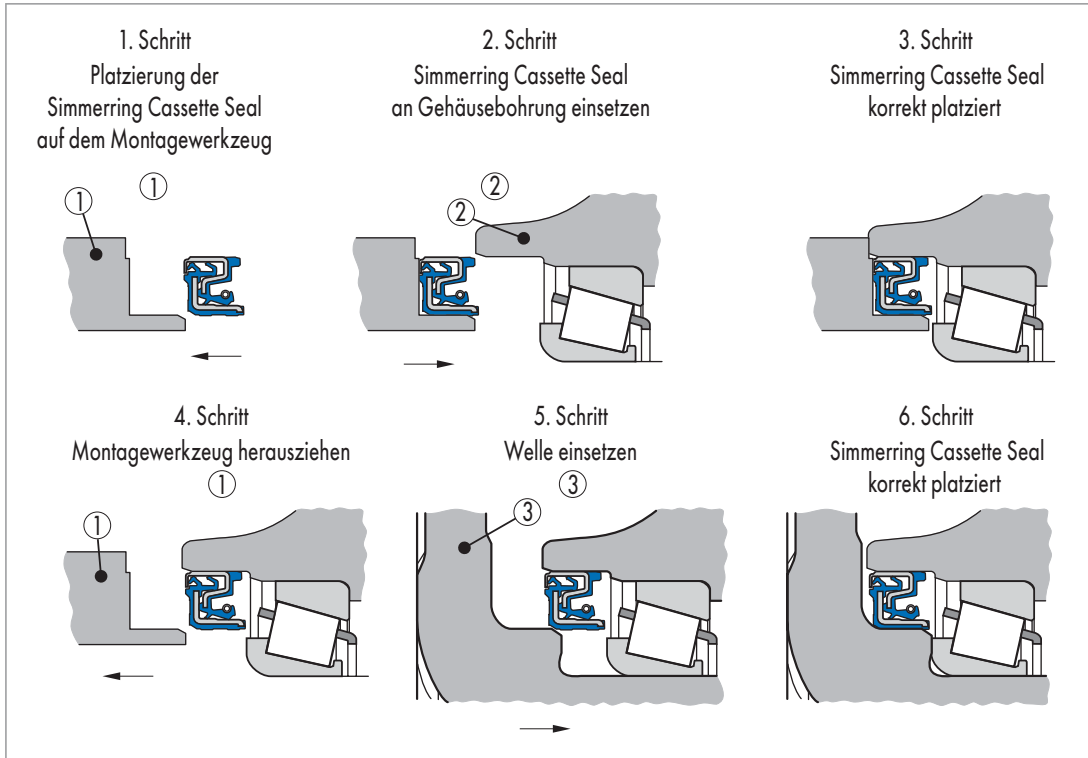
Montage von Simmerring Cassette Seal – Fall B (ohne “bearing stop“)
